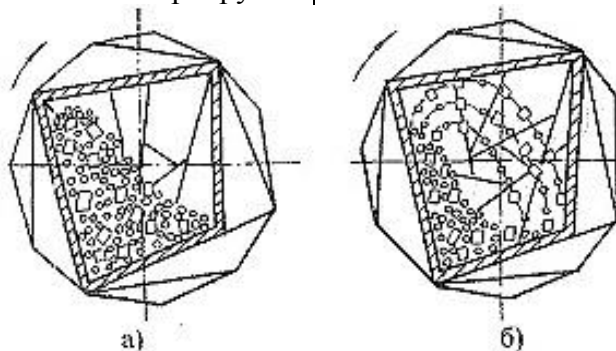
Схема движения рабочих сред и обрабатываемых деталей в винтовых роторах (поперечное сечение): а - лавинообразный режим работы; б - водопадный режим работы
